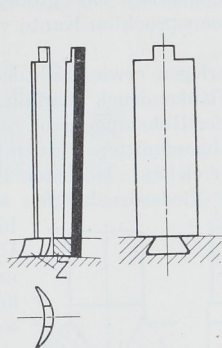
Schaufelbefestigung mittels Schwalbenschwanzes.
